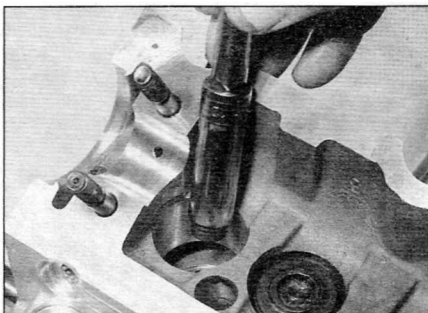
Установка маслоотражательного колпачка с помощью торцевой головки
